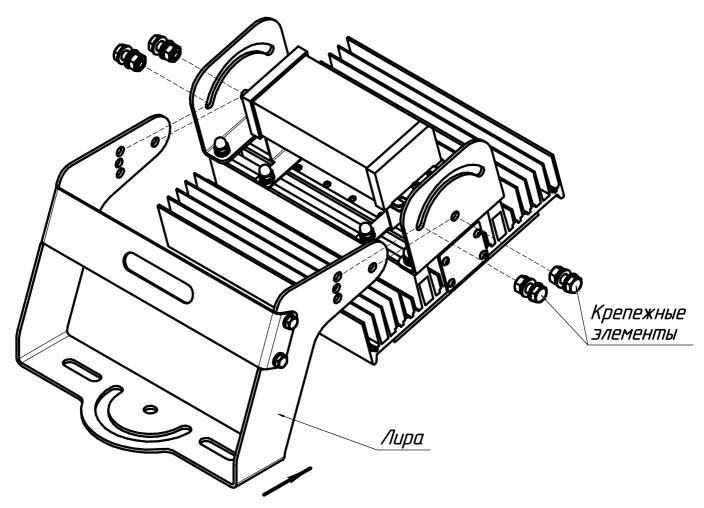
Схема установки узла крепления (лиры) на светильник
